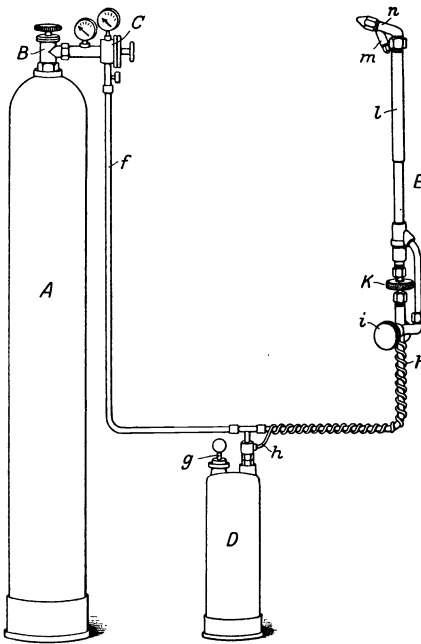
Benzol-Schweißeinrichtung.
